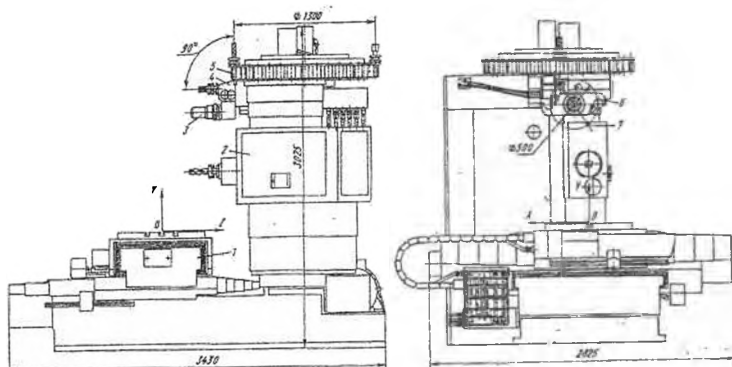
Багатоціповий горизонтально-фрезерний верстат з ЧПУ і МАЗІ, розташований на шпиндельній бабці
